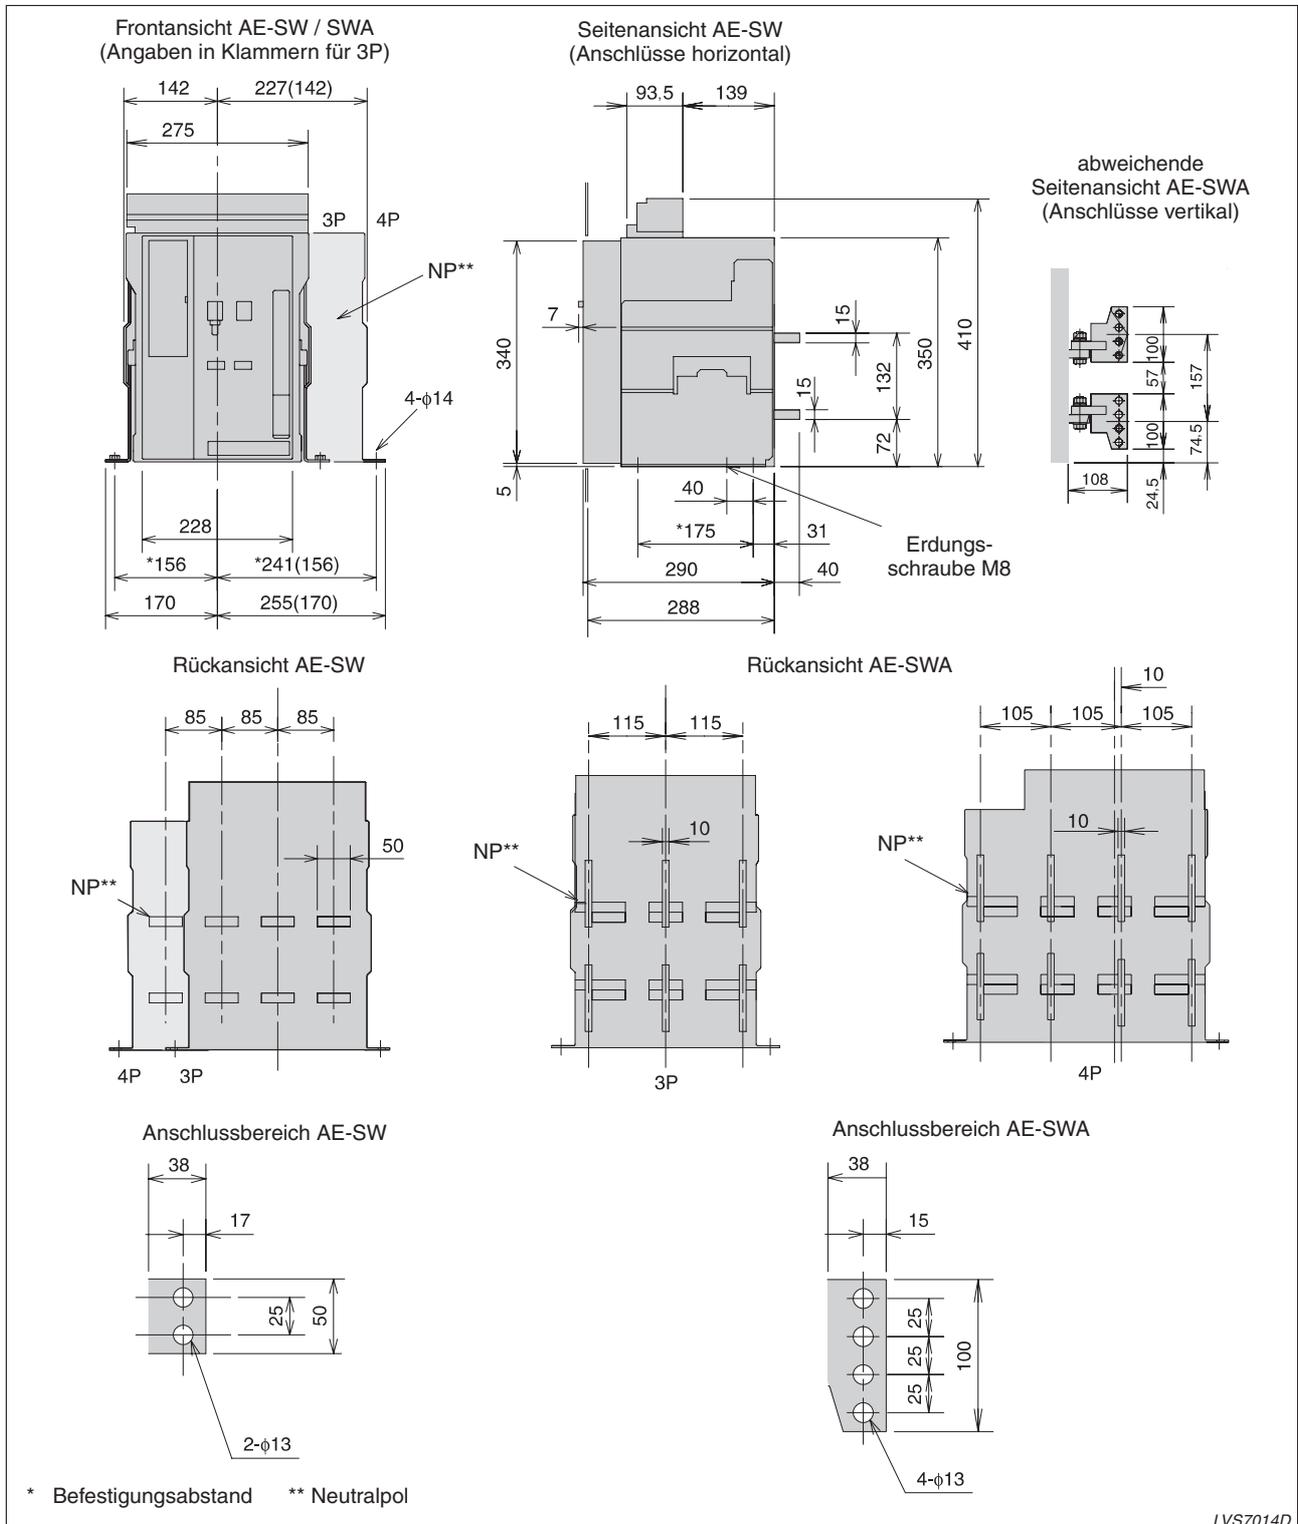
Abmessungen (in mm) der Schalter für Festeinbau
